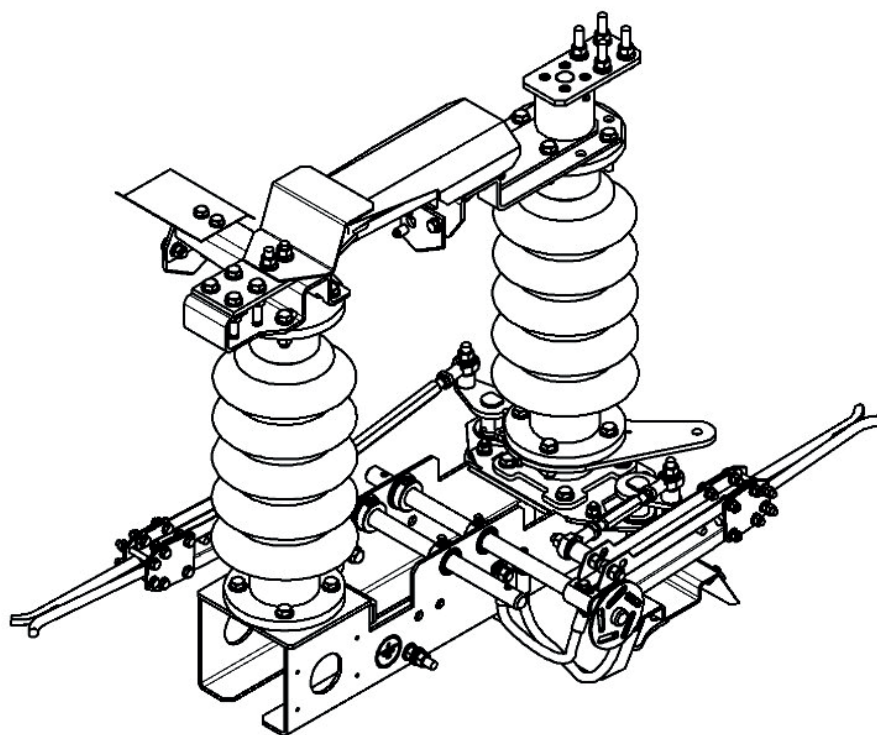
Устройство и основные части ведущего полюса разъединителя
